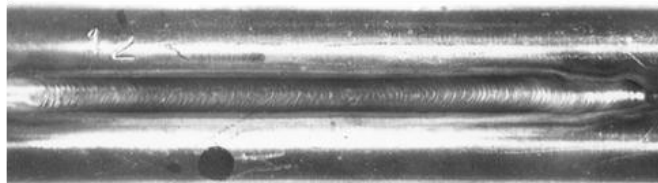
Сварной шов двух прутков стали ЧС-139 (плавка 4588)
